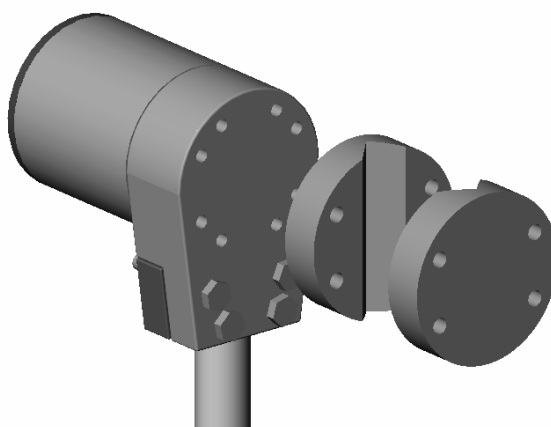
Démontez les cales de serrage de la barre de montage pour une installation sur le mixeur
